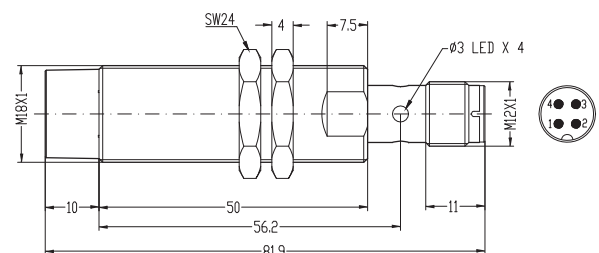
Lange Ausführung, Nicht bündiger Einbau, Steckversion
